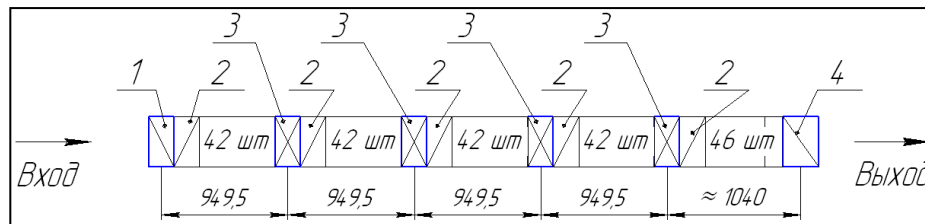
Схема расположения радиальных подшипников: 1 - нижний подшипник 2 - опора колеса 3-промежуточный радиальный подшипник 4- верхний подшипник
